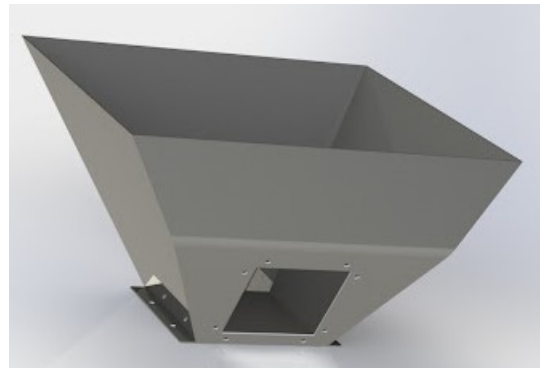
Diseño 3D del acople de tolva (Autoría propia)
